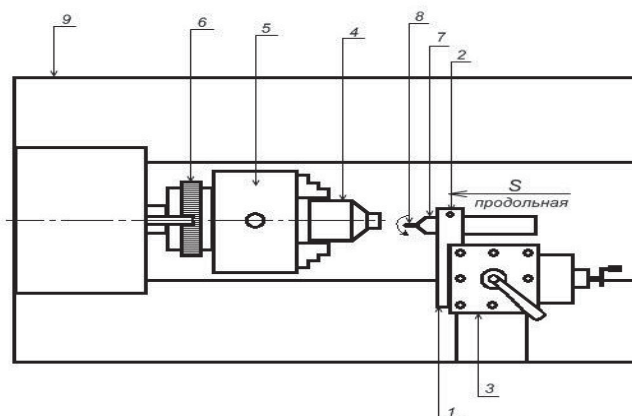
Схема универсального узла для обработки отверстий и пазов на торце детали
